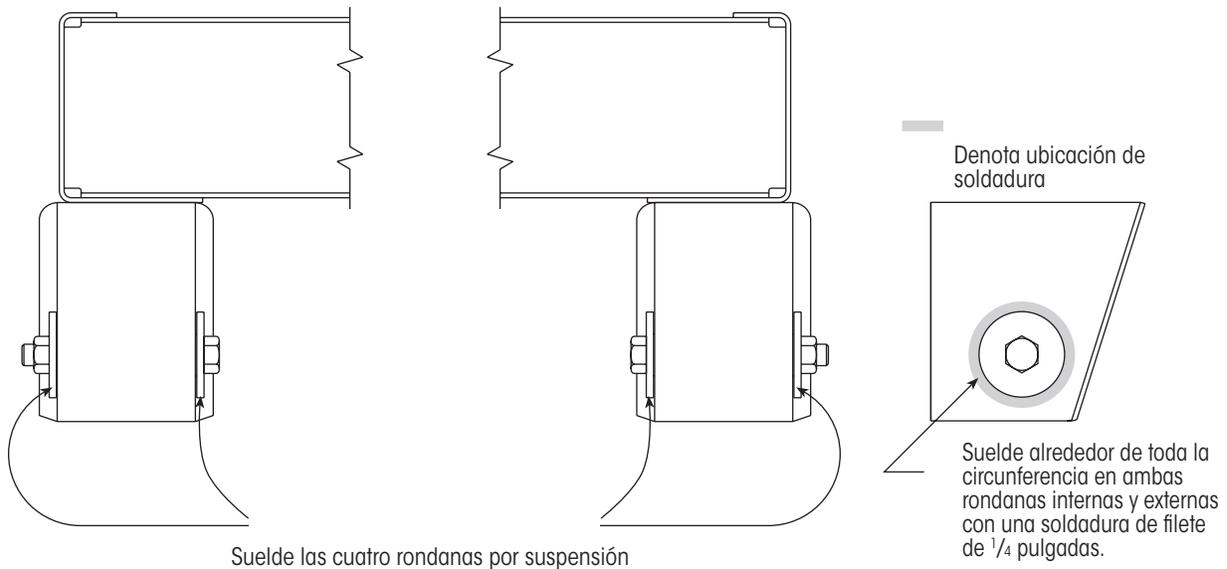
Ubicación de soldaduras en rondanas soldables
